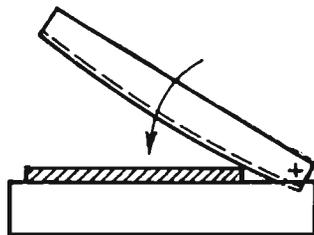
Схема резки поворотным ножом с криволинейной режущей кромкой
